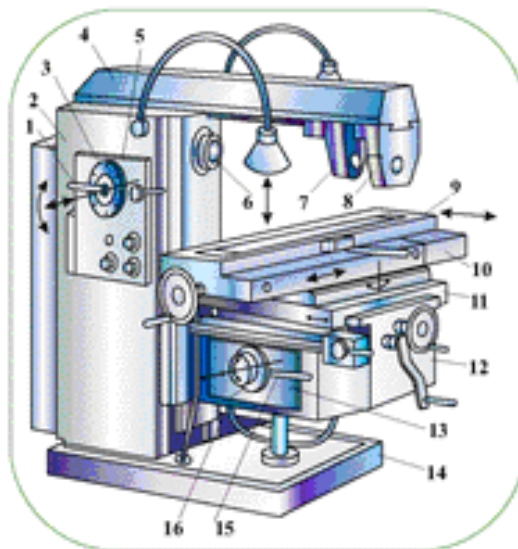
Внешний вид горизонтально-фрезерного станка серии 6М82
